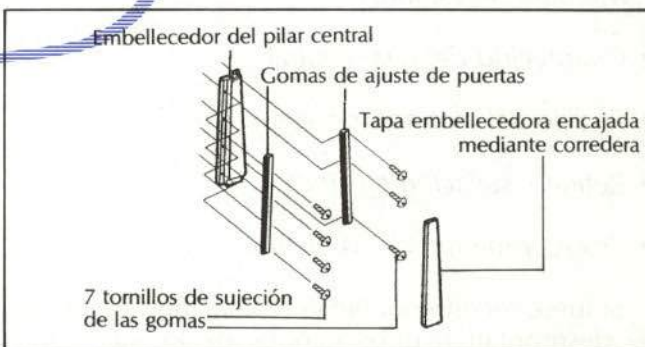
Sujeción de la moldura de ajuste de puertas.
